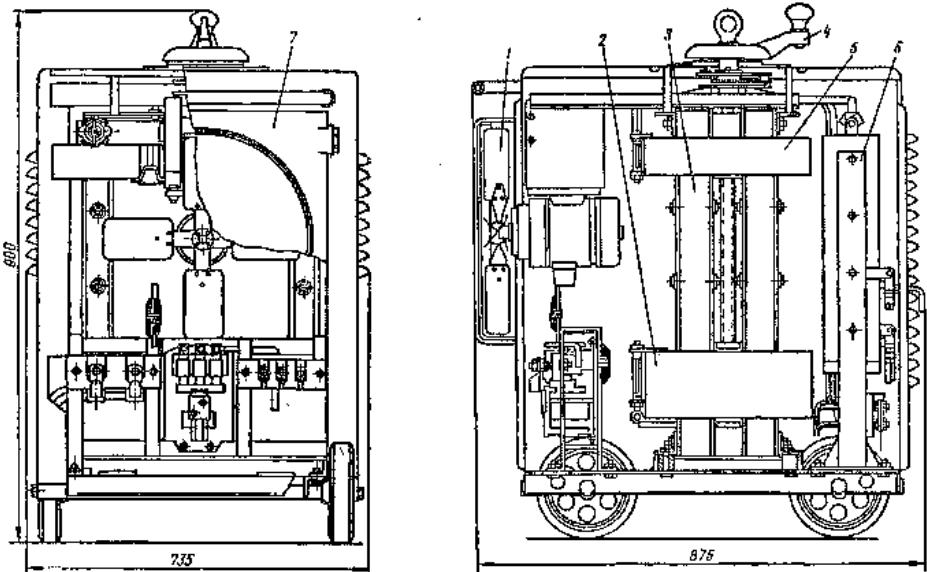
Конструктивное исполнение сварочного выпрямителя ВСС-300:
